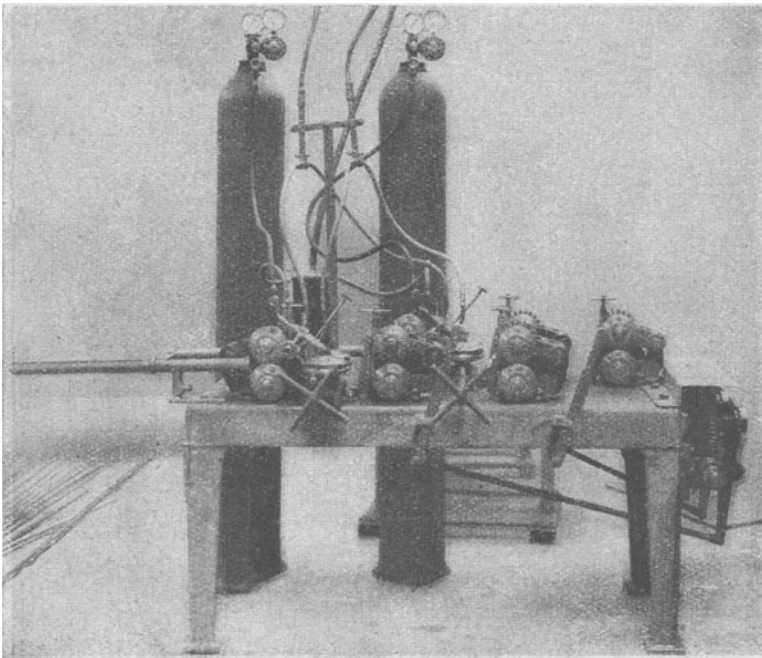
Autogene Rohr-Schweißmaschine.
